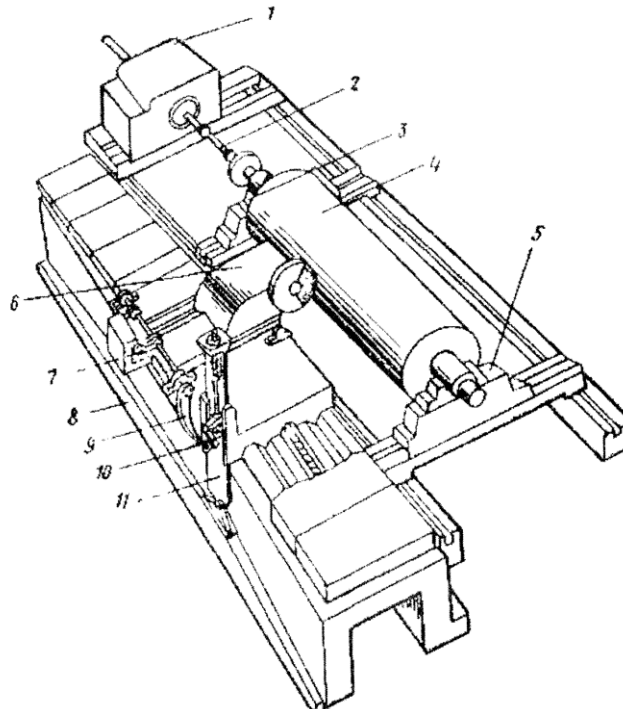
Компоновка вальцешлифовального станка с подвижной приводной бабкой:
